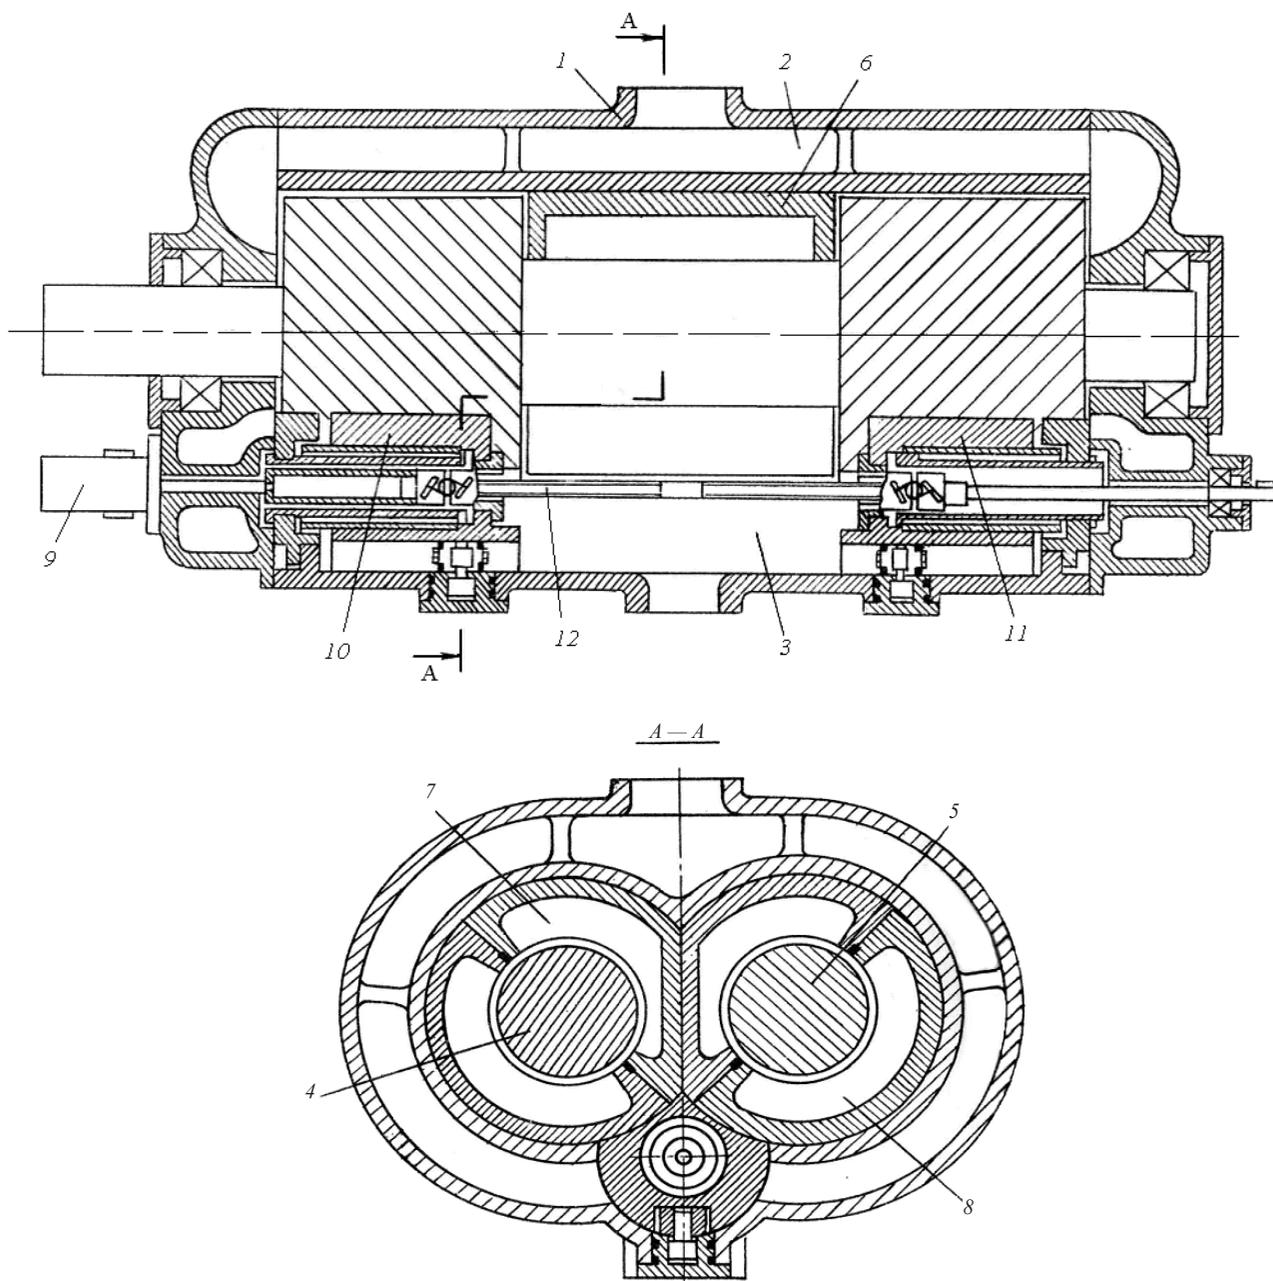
Схема винтового компрессора с разгрузочной камерой:
